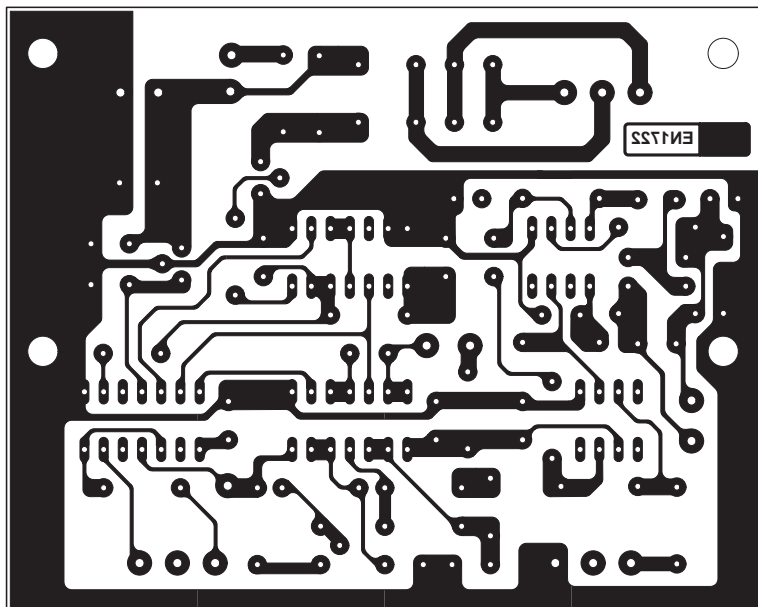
1 : Dessin, à l'échelle 1:1, du circuit imprimé double face à trous métallisés de la platine à ultrasons EN1722, côté soudures.
